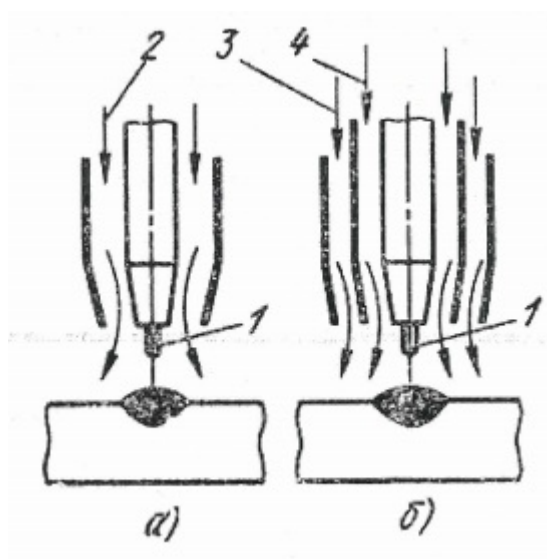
Централизованная подача защитного газа в зону сварки
